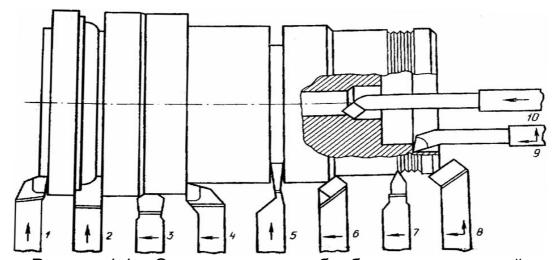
Основные схемы обработки поверхностей: 1 — подрезной резец; 2 — фасонный резец; 3 — резец для чистовой обработки (резец Колесова); 4 — резец проходной упорный; 5 — отрезной (канавочный) резец; 6 — проходной прямой резец; 7 — резьбовой резец; 8 — проходной отогнутый резец; 9 и 10 — расточные резцы
